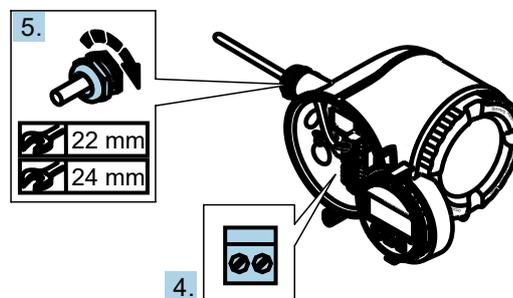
Raccordement des câbles et serrage des presse-étoupe
